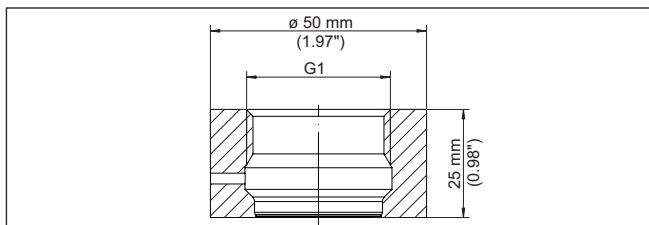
Dimensions raccord à souder G1 (ISO 228-1) - joint torique
